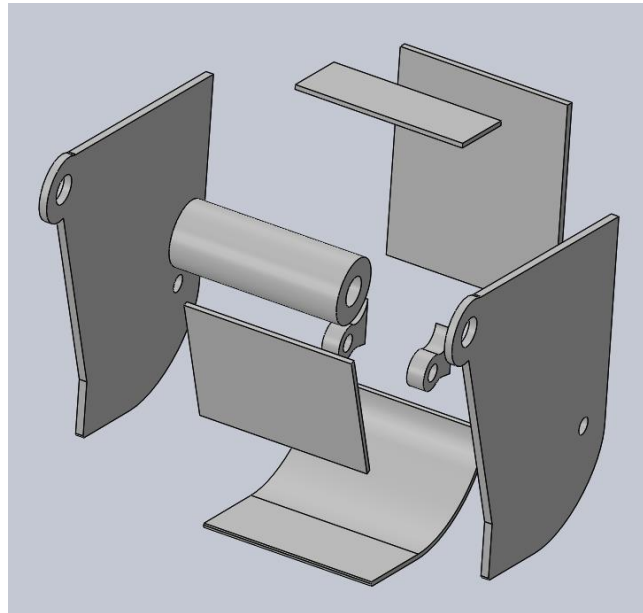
Vista explosionada del subensamblaje cuerpo central. [2]
